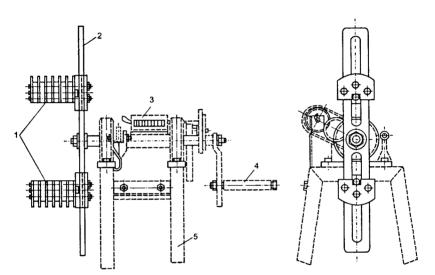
Станок для ручной намотки катушек с раздвижным шаблоном: 1 — колодка шаблона; 2 — диск; 3 — счетчик оборотов; 4 — рукоятка; 5 — станина
